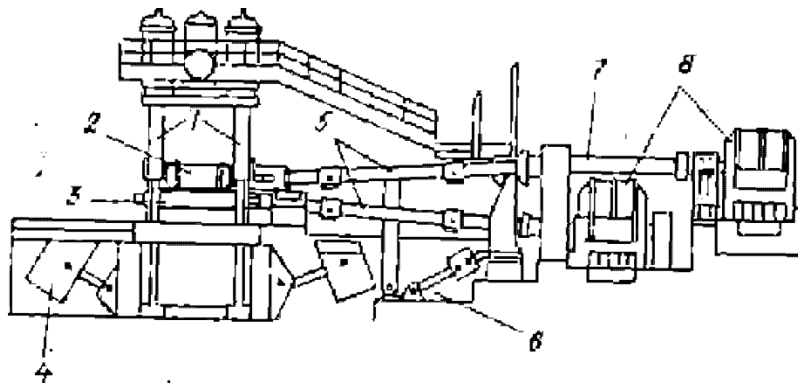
Схема блужінгу стану: 1 - робоча кліть; 2 - верхній валок; 3 - нижній валок; 4 - пристрій для зрівноважування верхнього валка; 5 - універсальний шпindel; 6 - пристрій для зрівноважування верхнього шпindеля; 7 - проміжний вал; 8 - головний електродвигун
